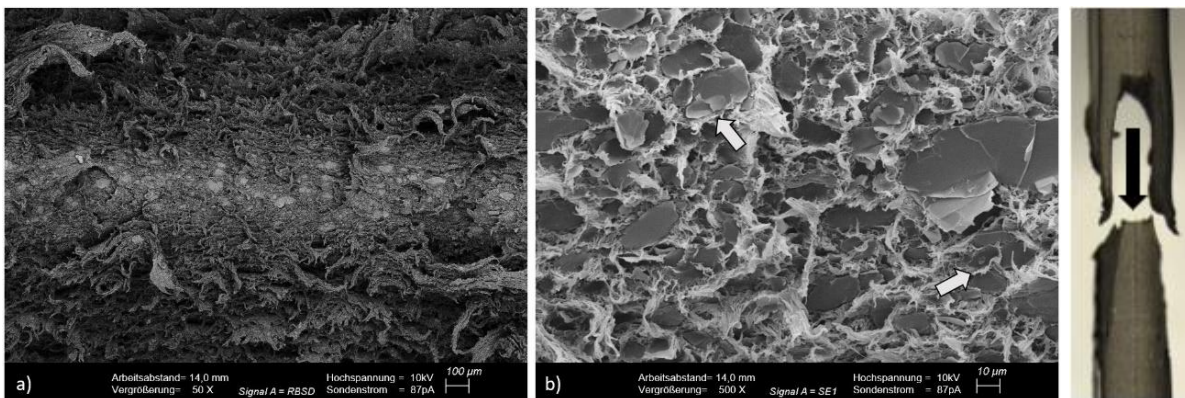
REM-RBSD-Aufnahmen der Bruchfläche in Draufsicht nach Zugversuch von Mat06; rechts: Illustration zur Aufnahmeorientierung; links: Übersicht; mittig: Detailaufnahme im Bereich der Seele des Bauteils (Zentrum) mit Markierung einiger Talkumplättchen
